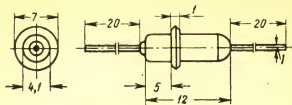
Габаритный чертеж диодов Д814А—Д814Д.
